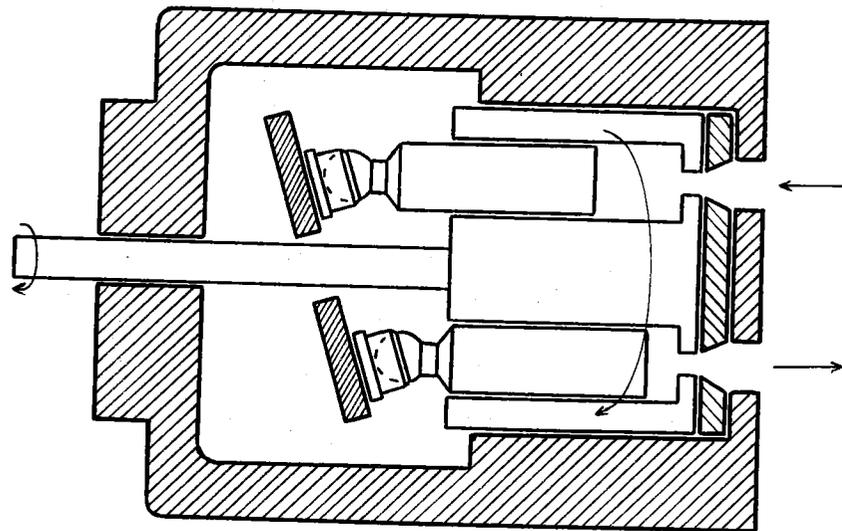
Sección longitudinal de una bomba de pistones axiales de cilindrada constante.
